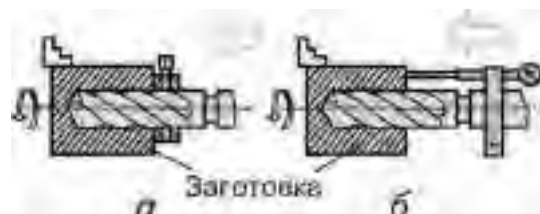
КОНТРОЛЬ ГЛИБИНИ ОТВОРУ ПІД ЧАС СВЕРДЛІННЯ.
